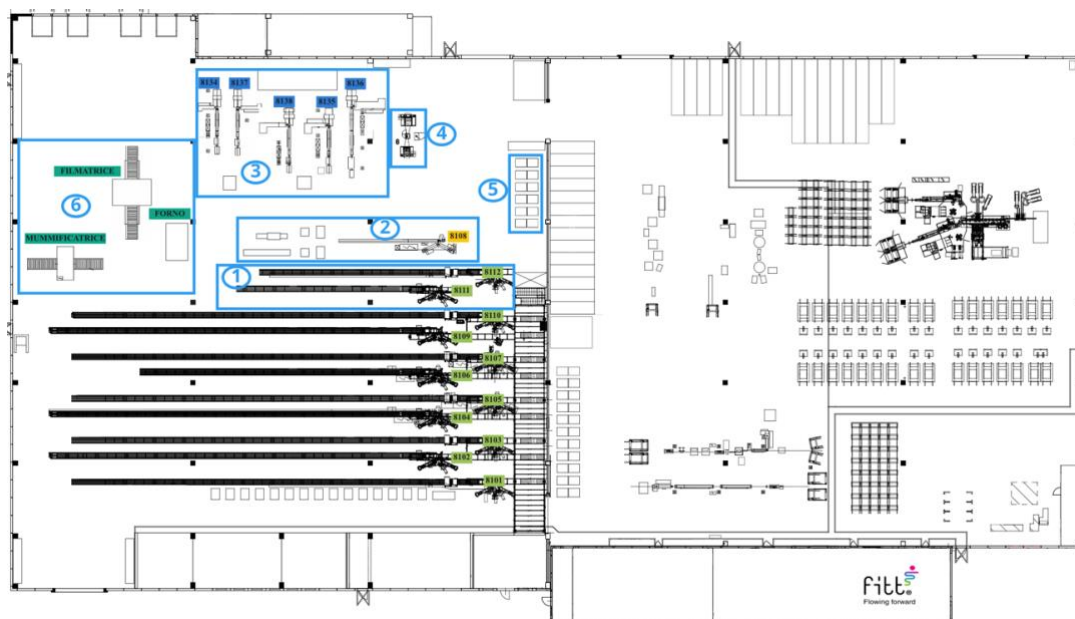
Pianta in scala della seconda ipotesi di re-layout (FITT, 2022)
